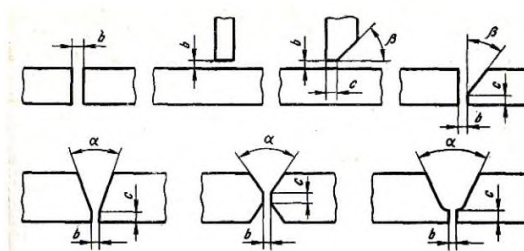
Конструктивные элементы разделки кромок и сборки под сварку
